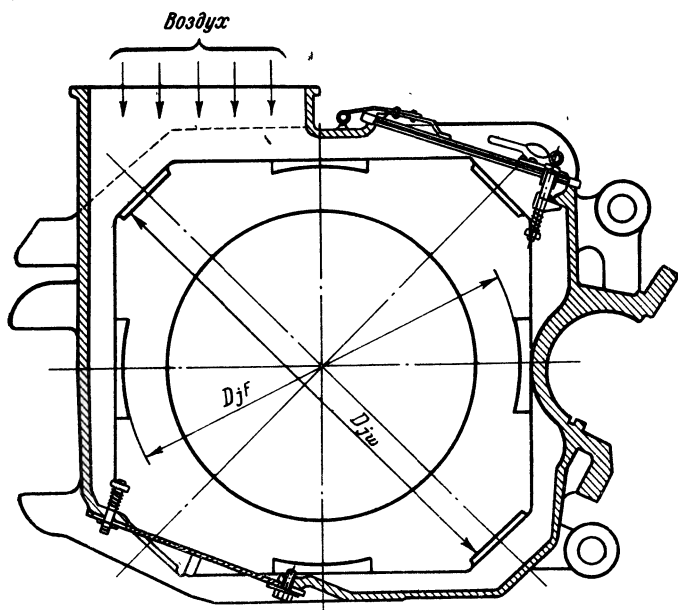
Станина тягового двигателя с горизонтальным расположением главных полюсов
